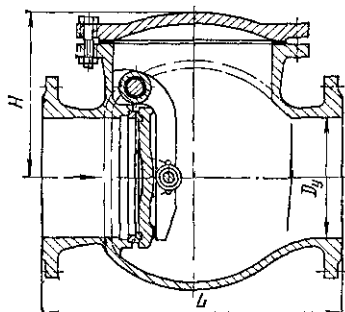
Клапан обратный поворотный фланцевый 19ч16р и 19ч16бр
